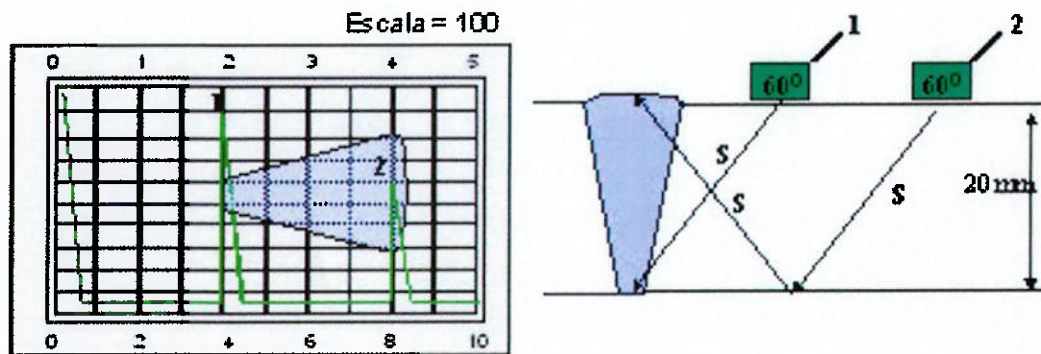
Inspeção em junta soldada por US [18].
